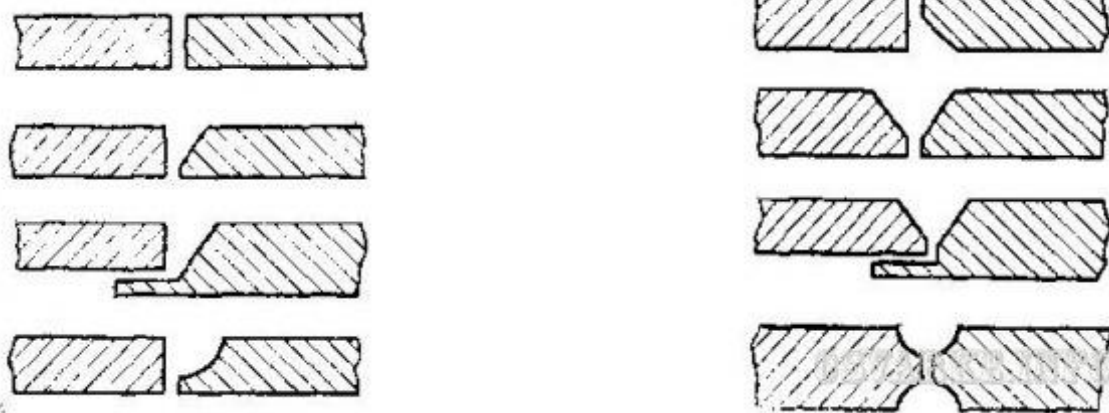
Форма подготовленных кромок под сварку для стыковых соединений
